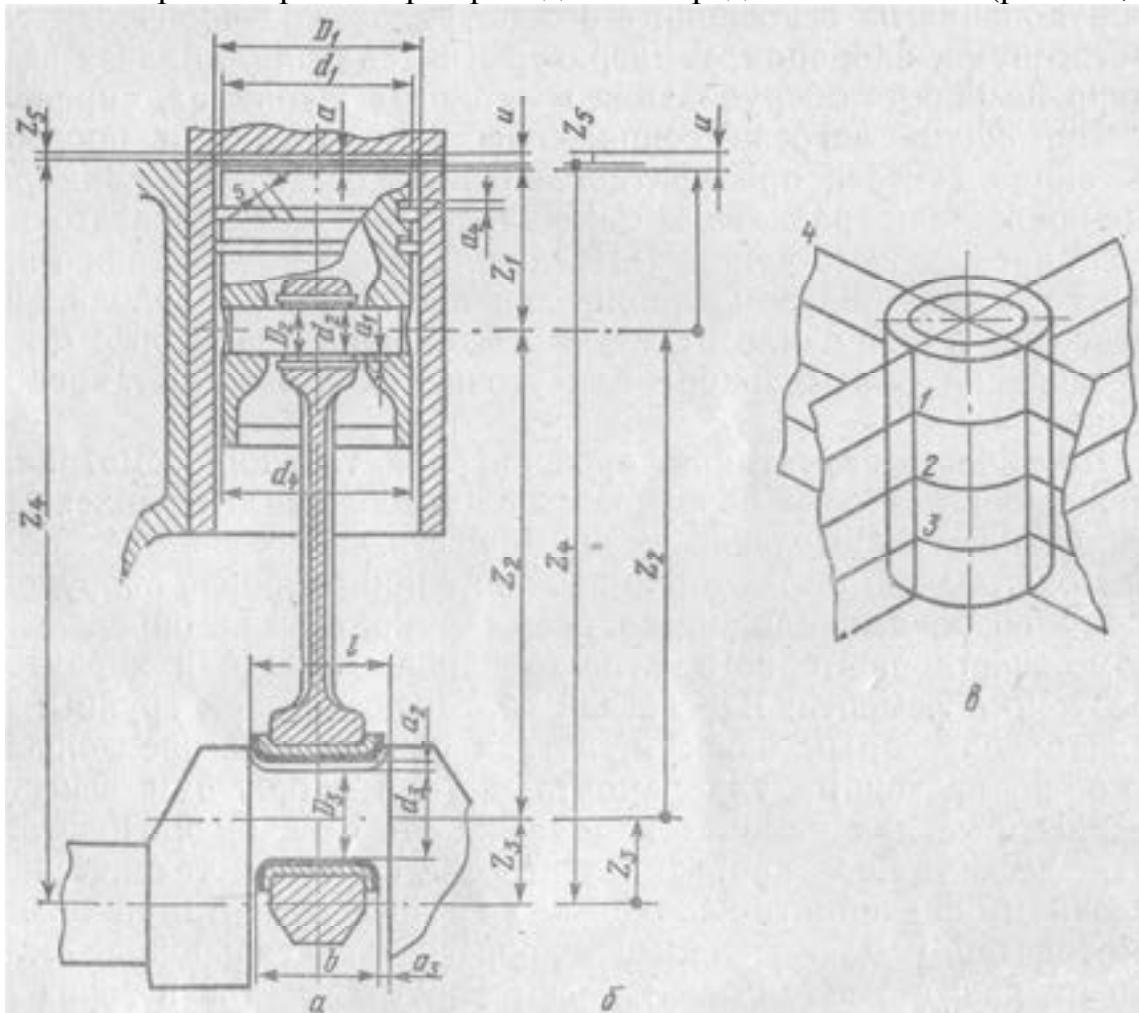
Схема обмера шатунно-поршневой группы (а) с упрощенной размерной цепью (б) и обмер втулок, пальцев и других деталей цилиндрической формы (в):
